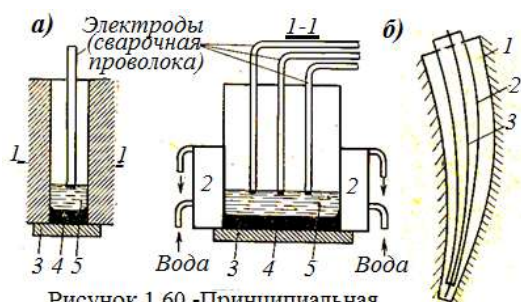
Принципиальная электрическая схема электрошлаковой сварки (ЭШС): а - сварка плавящейся проволокой, б - плавящимся мундштуком
